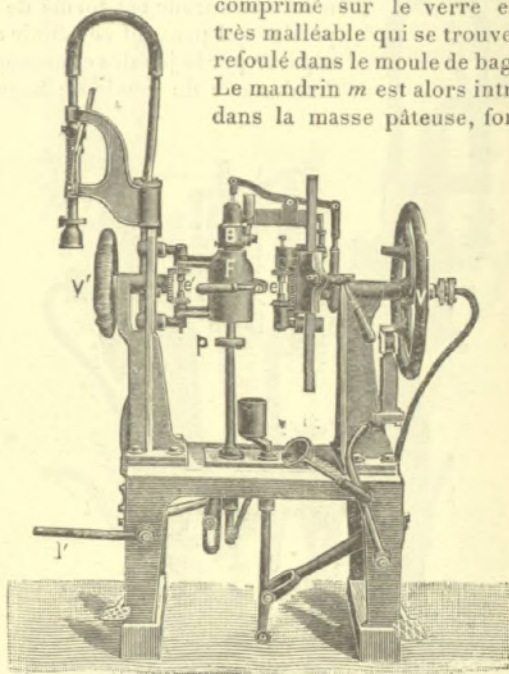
Machine C. Boucher pour la fabrication mécanique des bouteilles.
